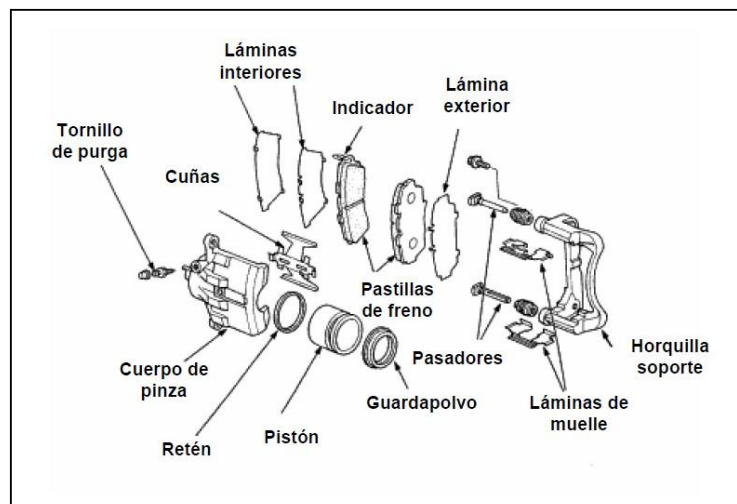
Plano de despiece del conjunto pinza flotante-pastillas.
